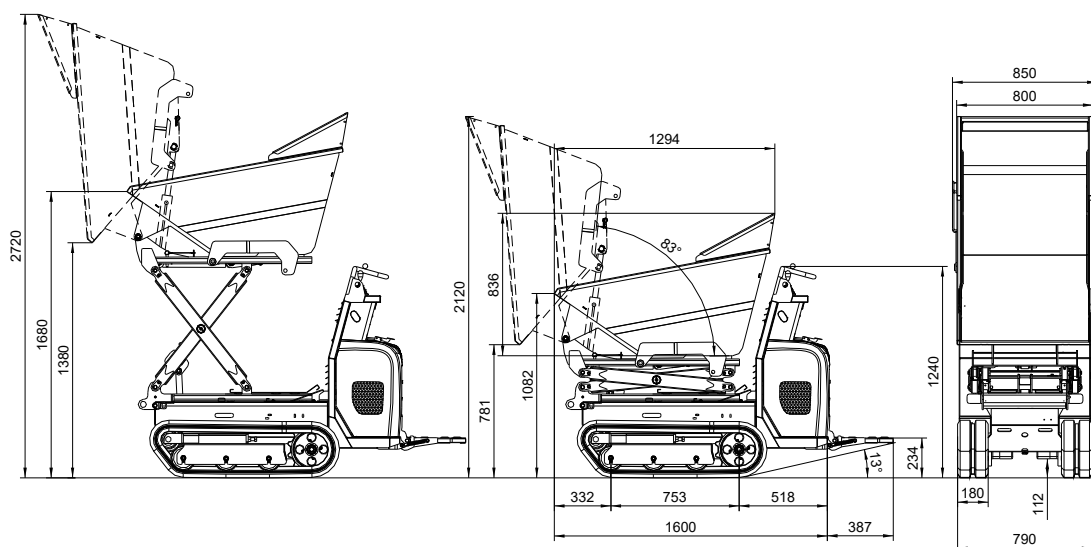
Dimensions de la machine (modèle DT08-D avec benne surélevée)
